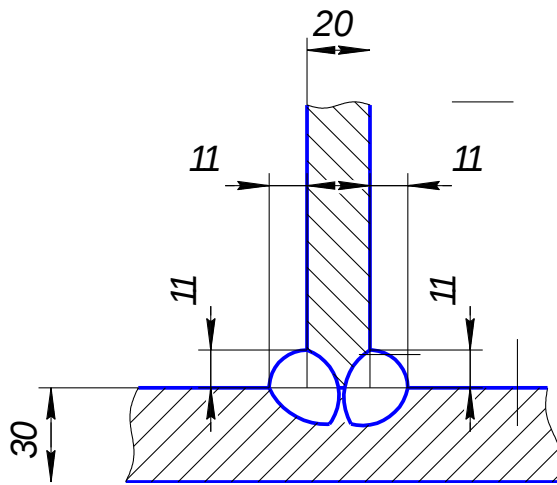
Конструктивні елементи з'єднання ТЗ
